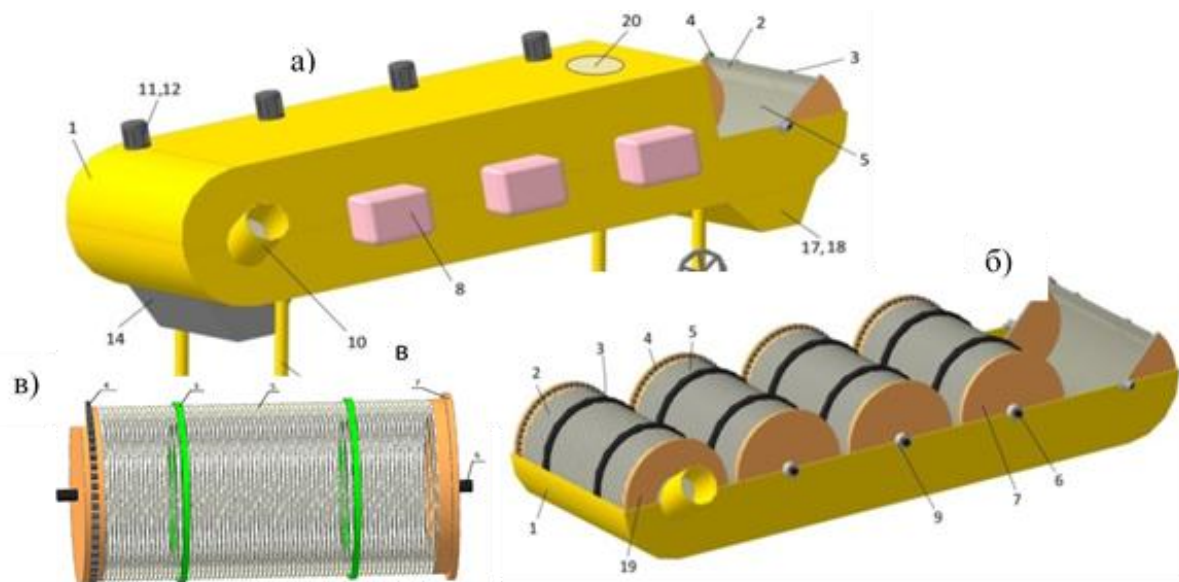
СВЧ установка с цилиндрическими резонаторами в виде винтового шнека:
